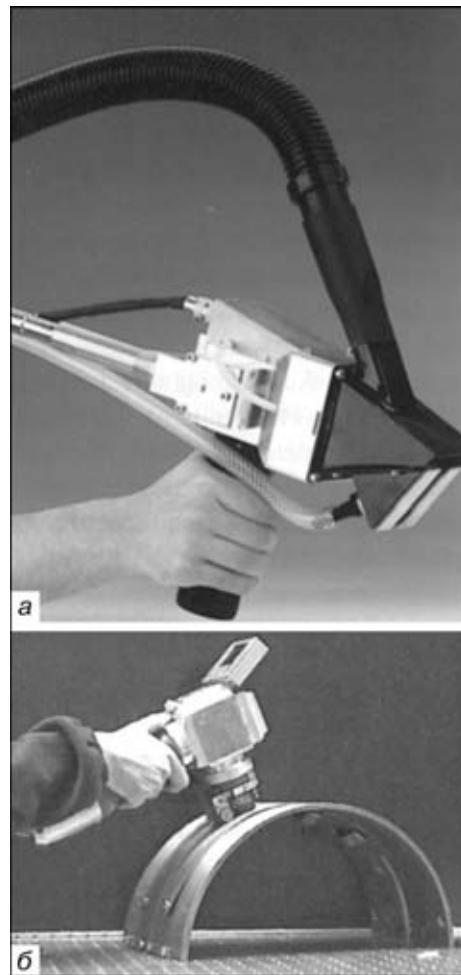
Ручной инструмент мобильной лазерной установки для очистки поверхностей (а) и сварки (б)
